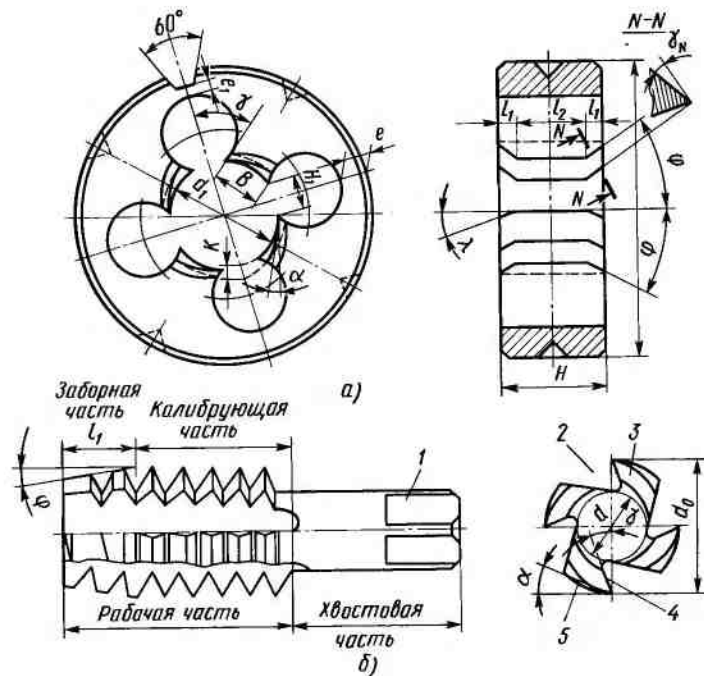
Конструкция плашки (а) и метчика (б)
